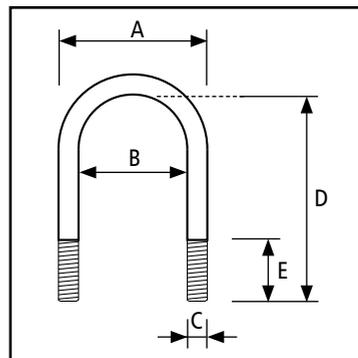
, Außenbreite (A), Innenbreite (B), Gewindedurchmesser (C), Bügelhöhe bis Unterkante Bügel (D) und Gewindehöhe (E)
